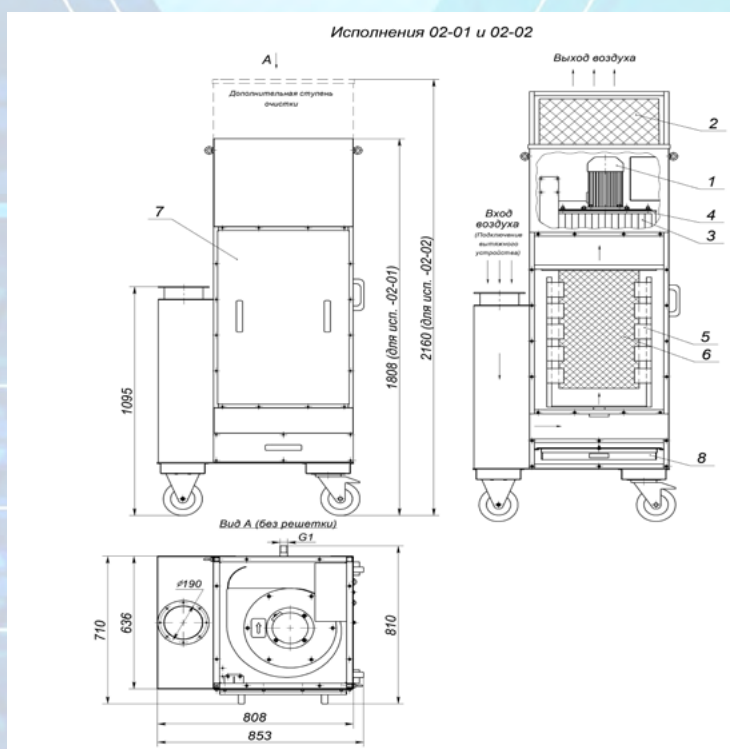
Схема агрегата ПАР-ПМ (исполнения 02-01 и 02-02)
